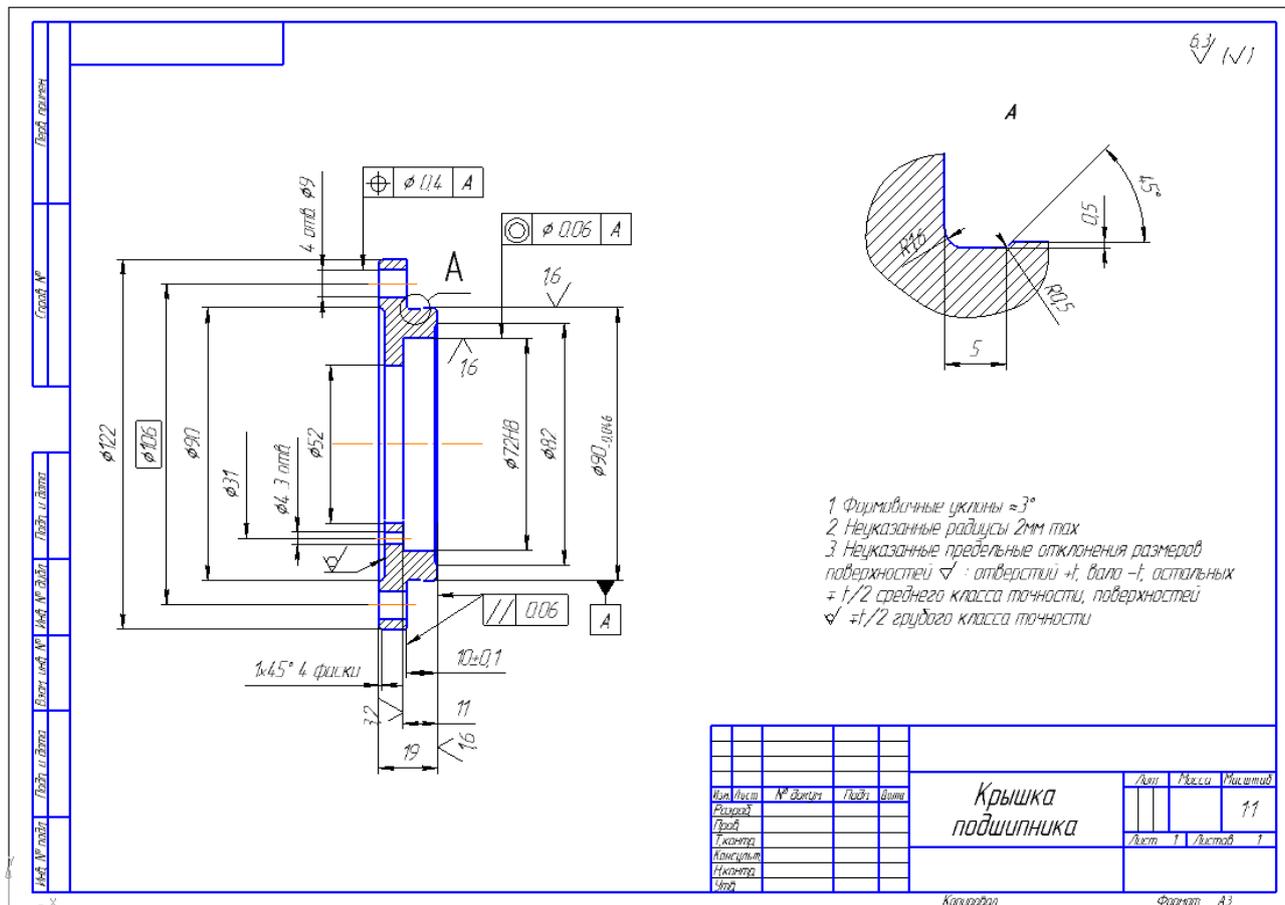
Рабочий чертеж крышки подшипника сквозной.
